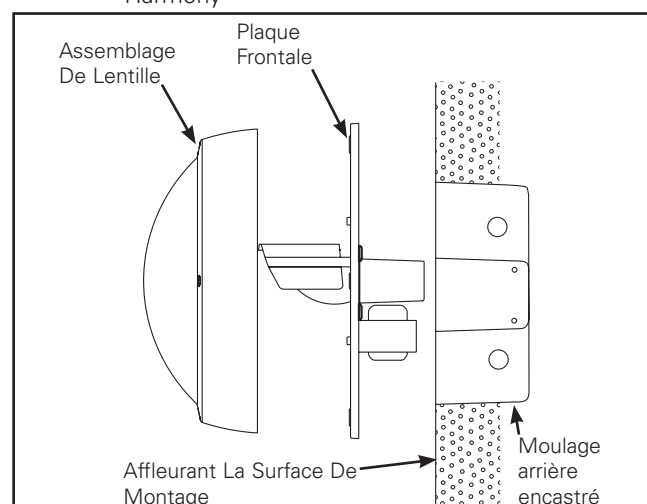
Assemblage Lentille/Plaque Frontale Pour Modèles Terrapin™
